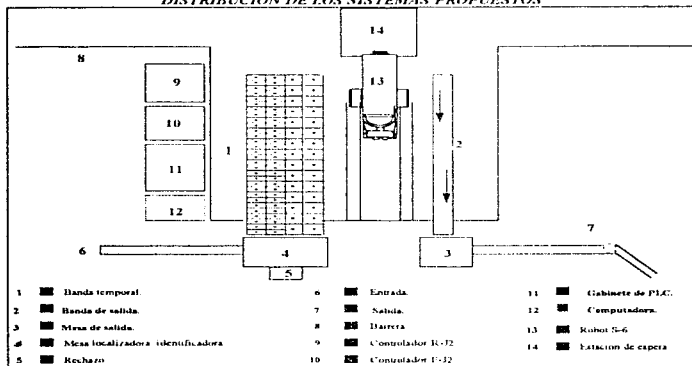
Sistemas de control que se encuentran en la Planta
